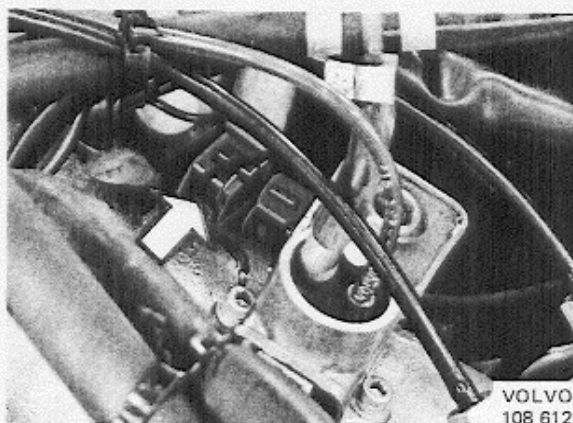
Anschluß des Kontaktsteckers, Steuerdruckregler
